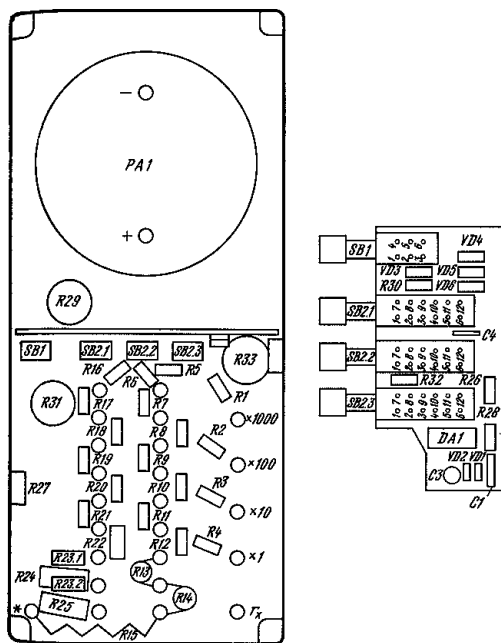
Схема расположения элементов комбинированного прибора И20-05
